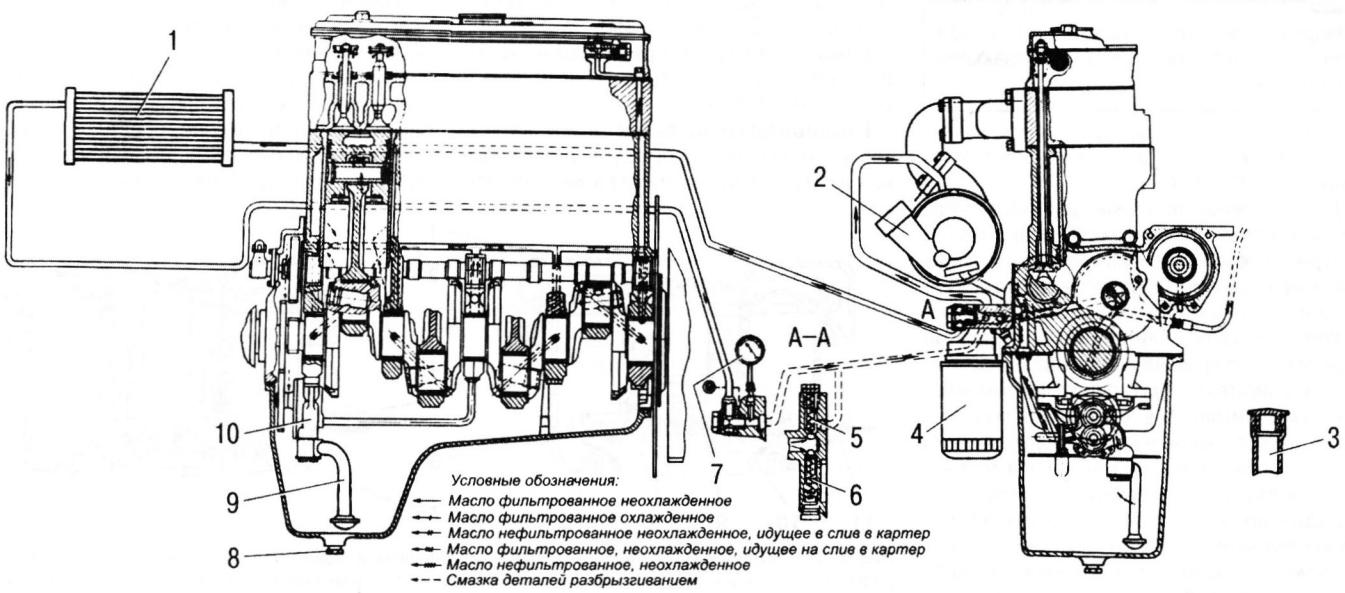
Система смазки: 1 – масляный радиатор; 2 – турбокомпрессор; 3 – маслоналивная горловина; 4 – масляный фильтр; 5 – редукционный клапан; 6 – сливной клапан; 7 – датчик указателя давления масла; 8 – пробка масляного картера; 9 – маслоприемник; 10 – масляный насос
